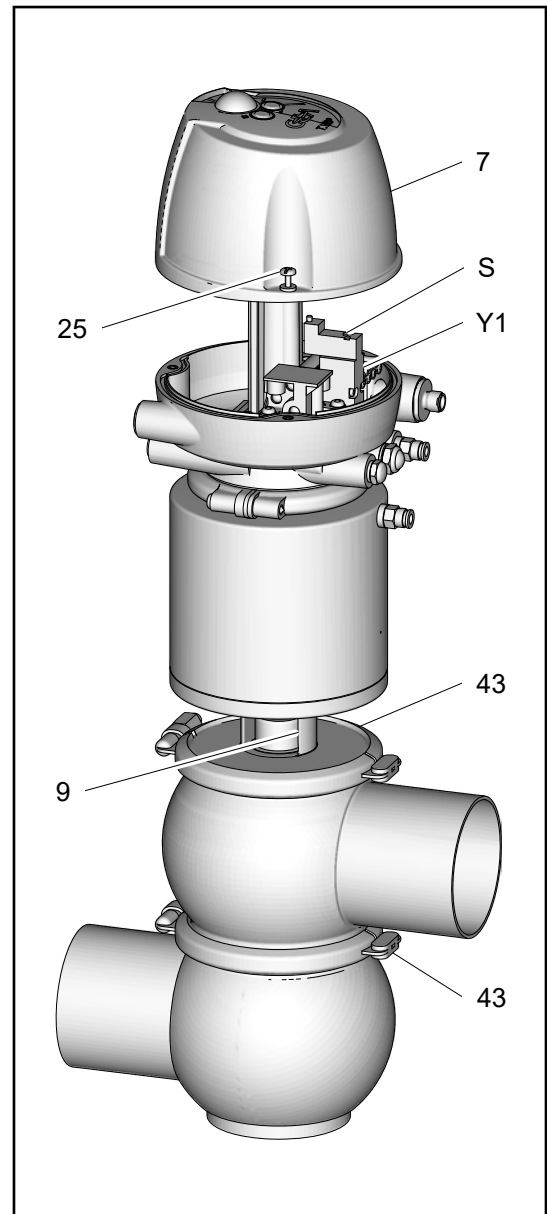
Ausführung mit 2 Gehäusen
